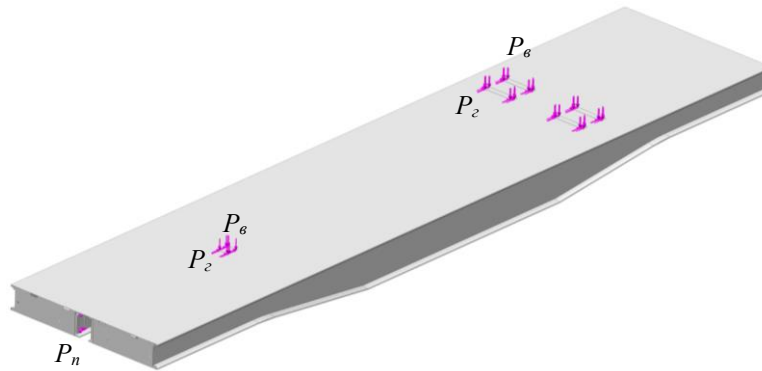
Розрахункова схема несучої конструкції вагона-платформи
